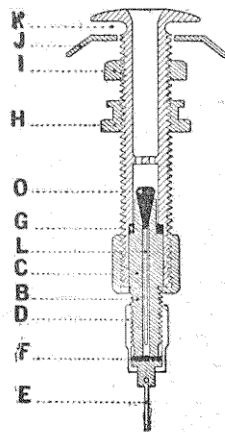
Coupe de valve Michelin pour pneu de motocyclette.
